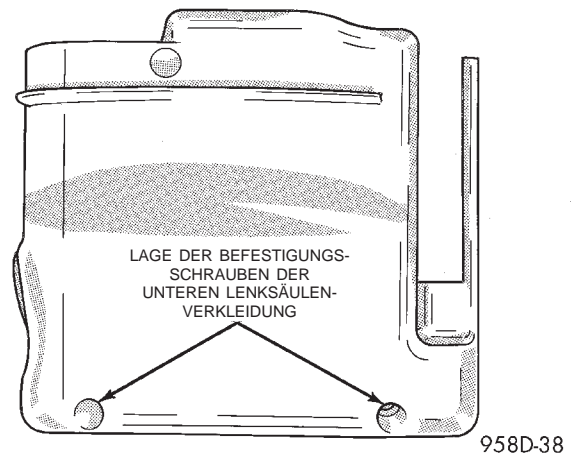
Lage der Befestigungsschrauben der unteren Lenksäulenverkleidung
